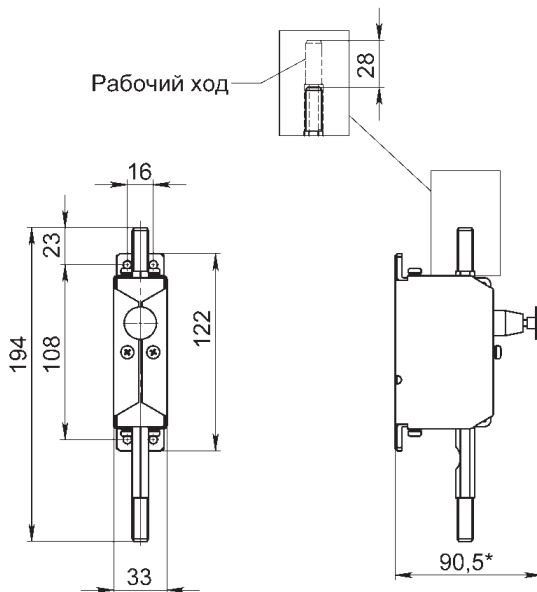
Габаритные, присоединительные и установочные размеры БК
